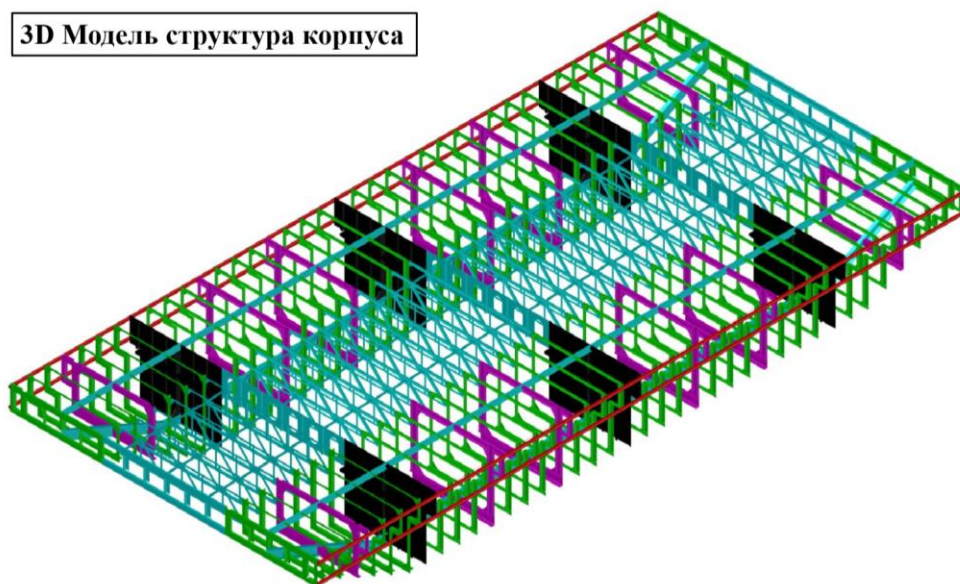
3D модель конструкции корпуса плавучего отеля
